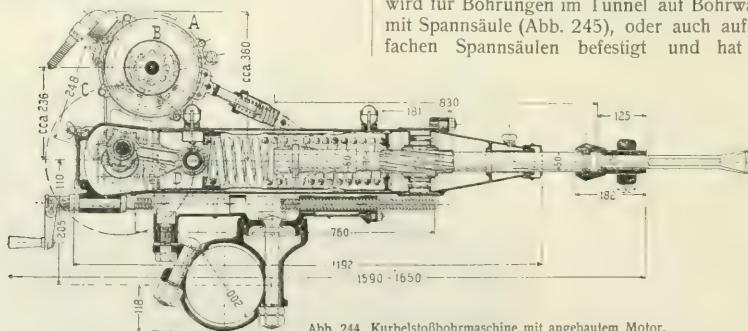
Kurbelstoßbohrmaschine mit angebautem Motor.
